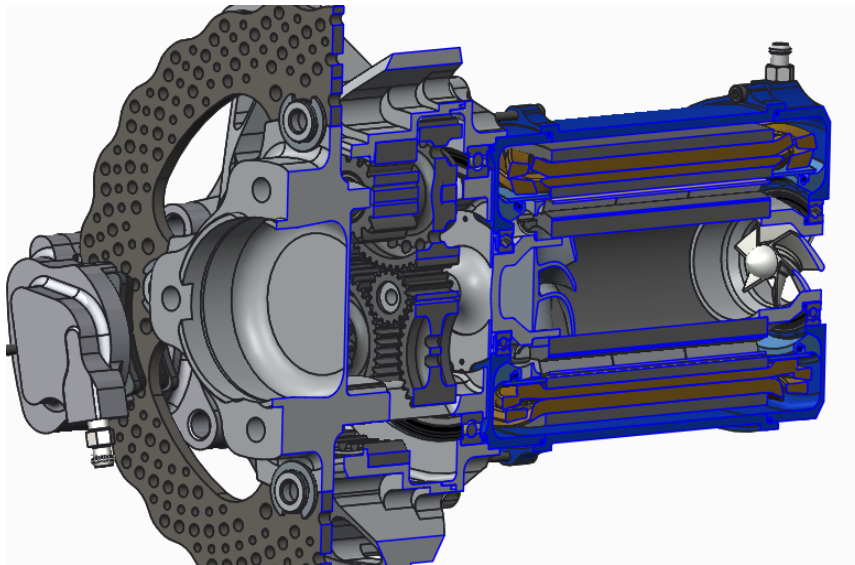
Vue en tranche de l'assemblage du porte moyeu
